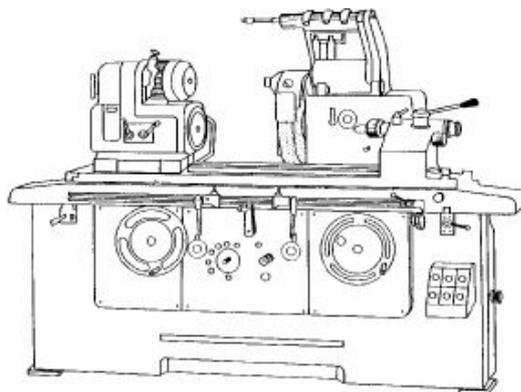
Retificadora cilíndrica universal. Fonte - IPB
